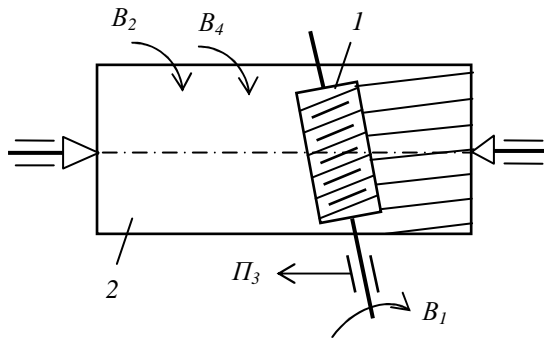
Способ фрезерования червячной фрезой шлицевых валов
